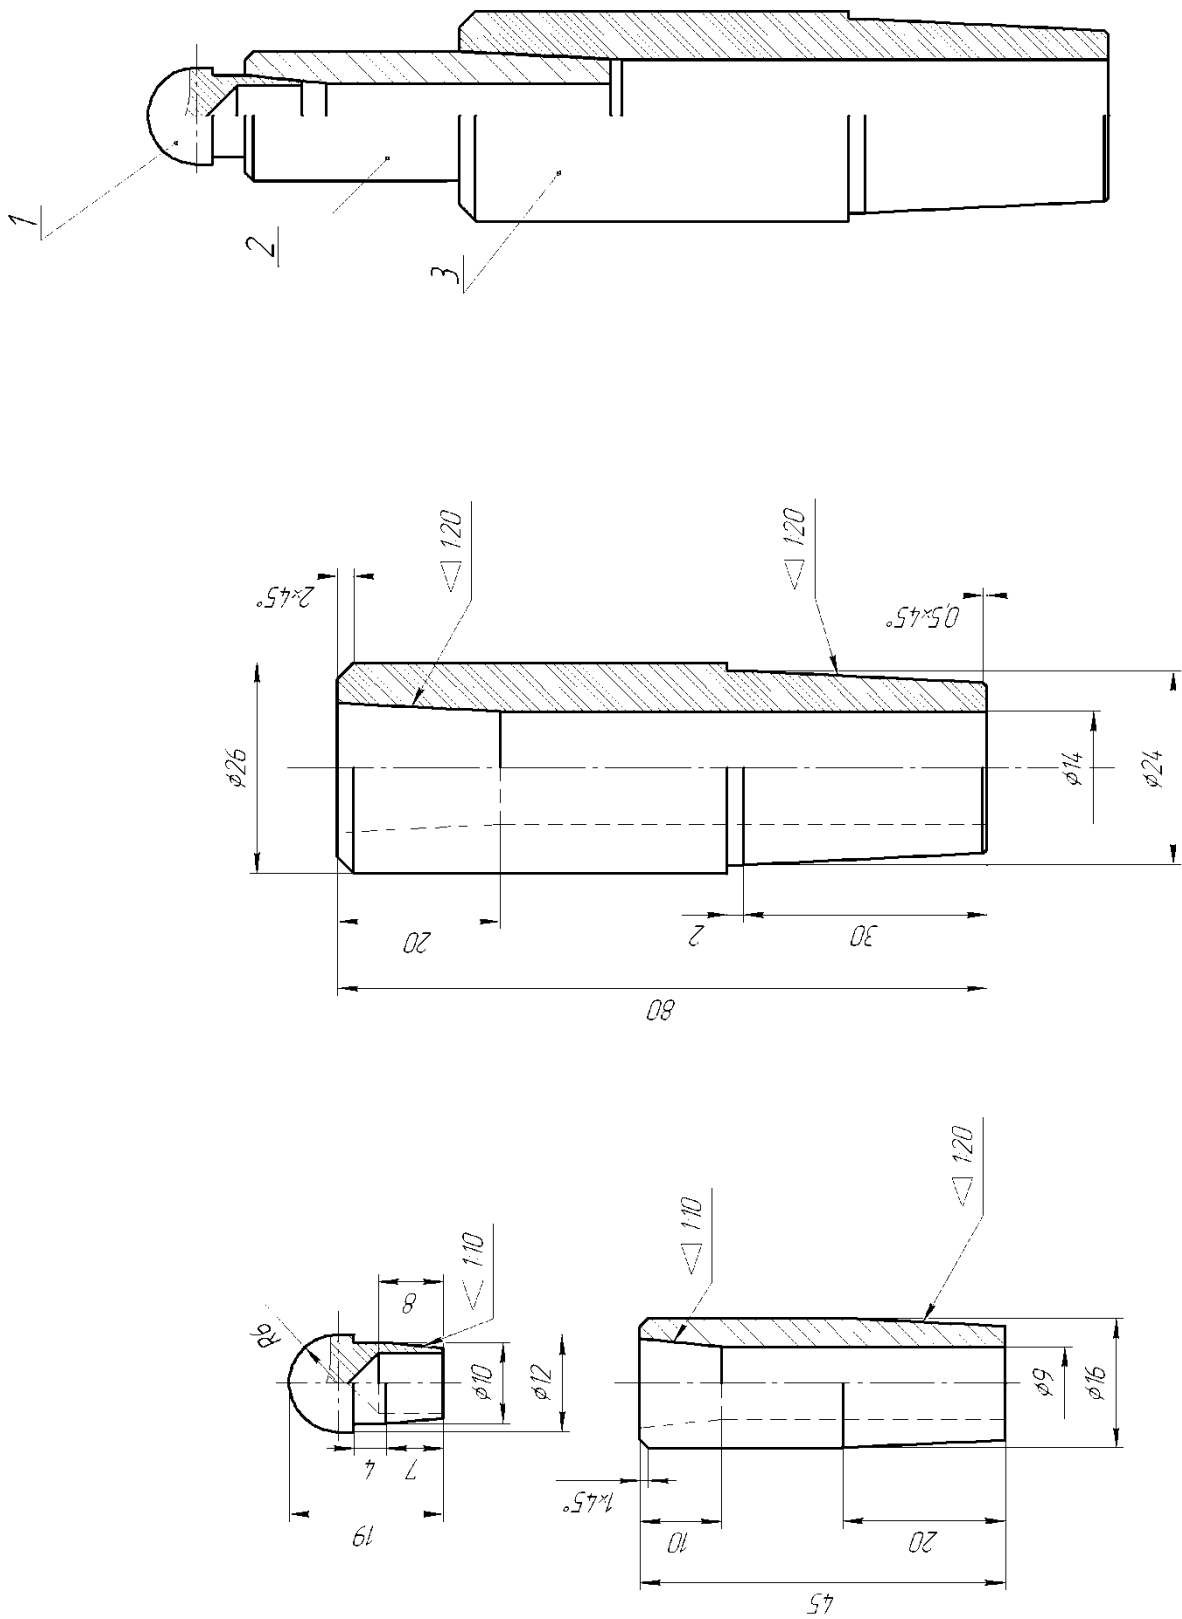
Базовый вариант электродов для точечной сварки
